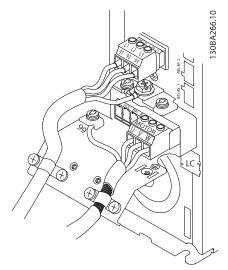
Befestigung der Zugentlastungsklemme
